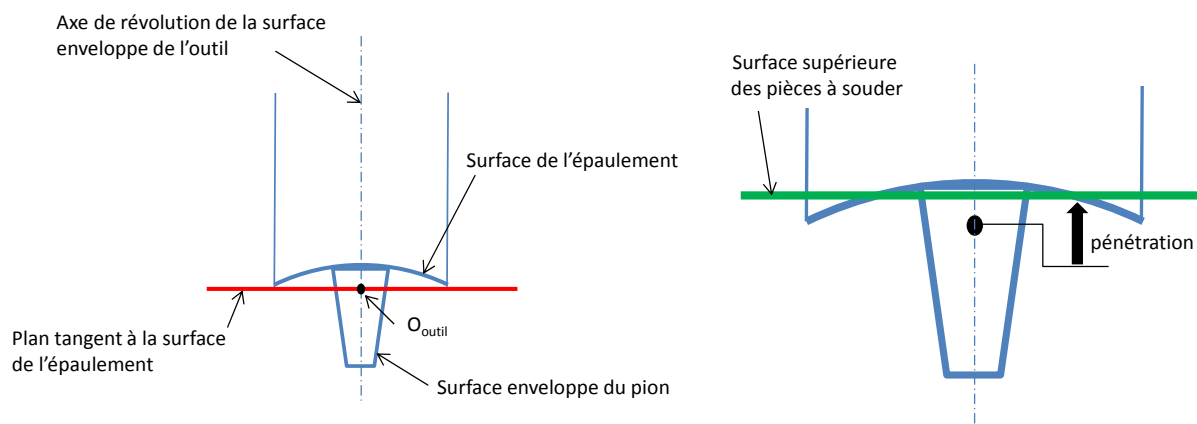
Définition géométrique du centre outil et position du centre outil en cours de soudage
